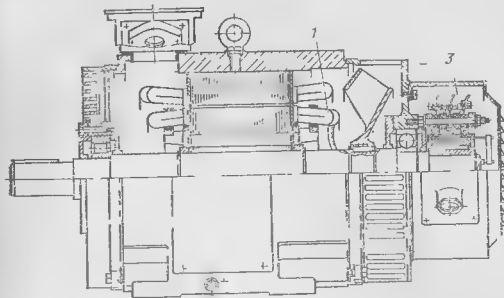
Асинхронный двигатель с фазным ротором 4АНК160.
